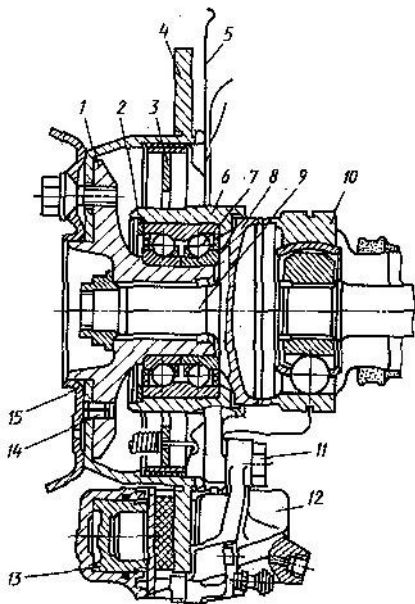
Опора подшипника заднего колеса автомобилей «Мерседес 190/190Е» с подшипником и тормозом. К подвижному шарниру равных угловых скоростей 10 приварен встык вал 9 колеса, который через мелкошлицевой профиль передает тяговый момент дальше на ступицу 1, установленную в радиально-упорном шариковом подшипнике 7, не требующем обслуживания. Целое наружное кольцо фиксируется в опоре 6 подшипника колеса стопорным кольцом 2. Уплотнительные кольца установлены с обеих сторон подшипникового узла, снабженного долговечным смазочным материалом. Дополнительной защитой от грязи служит с наружной стороны щиток 5 (охватывающий тормозной диск 4), а с внутренней — пояс 8 шарнира равных угловых скоростей. Этот пояс входит в выемку на опоре 6 подшипника колеса и образует лабиринт; дополнительное проникновение грязи и воды предотвращается центробежным действием этого колпачка. Тормозной диск 4 прижимается
